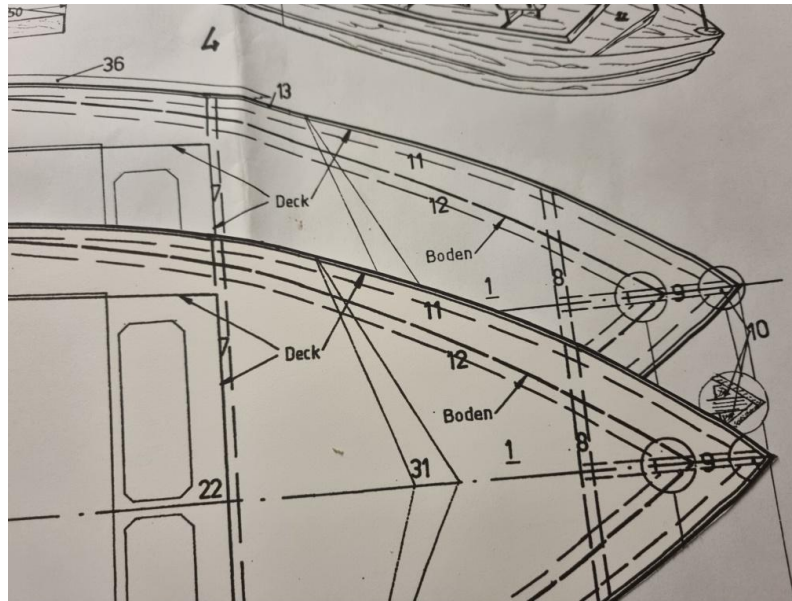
Bauplan (oben) und Decksschablone unten. An der Decksschablone sind umlaufen noch 1.5 mm abzutrennen! Ferner ist der Decksausschnitt noch auszuschneiden, über den später die im Bootsrumpf einzubauende Technik erreichbar ist.
